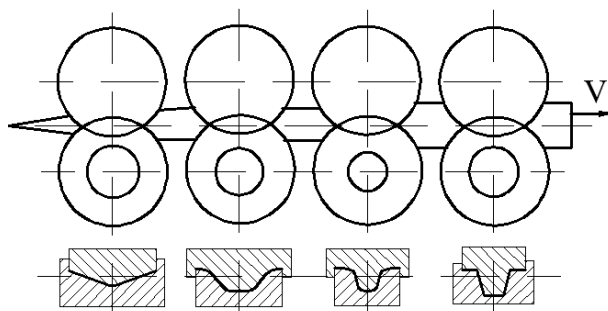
Схема гибки-прокатки в роликовом инструменте
